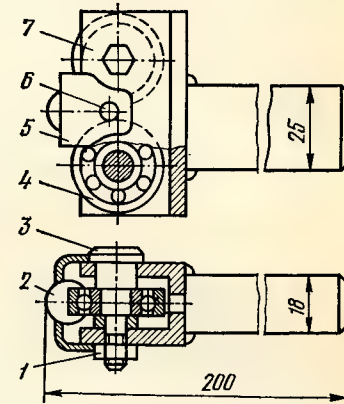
Шариковая накатка: 1 — гайка, 2 — шарик, 3 — ось, 4 — шарикоподшипник, 5 — обойма, 6 — винт, 7 — корпус
